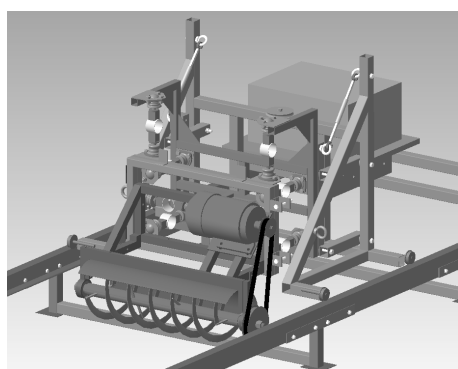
Лабораторный стенд с фрезерным рабочим органом
